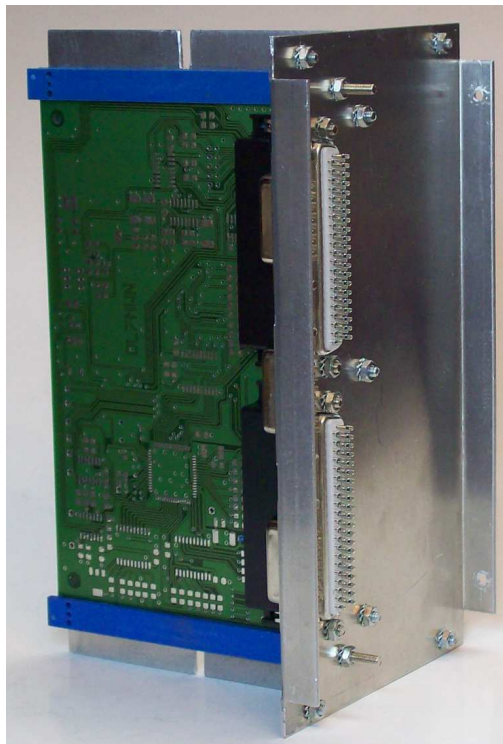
Montageblech 1 von unten mit eingeschobenem, unbestücktem Steuerrechner
